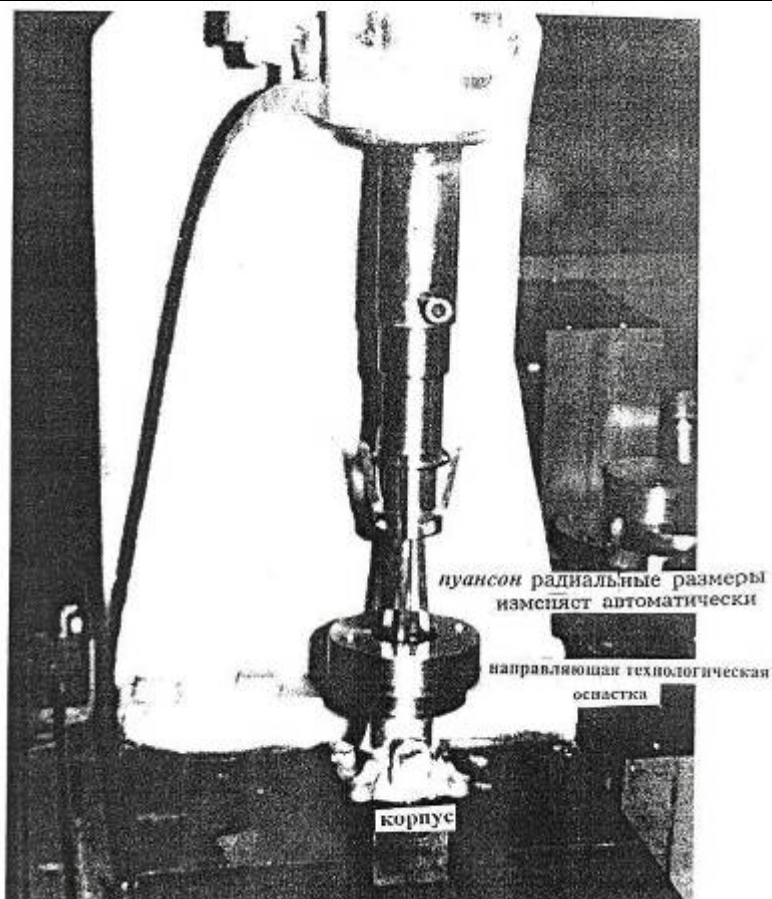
Широкоуниверсальный автоматический самопереналаживающийся сборочный центр.
